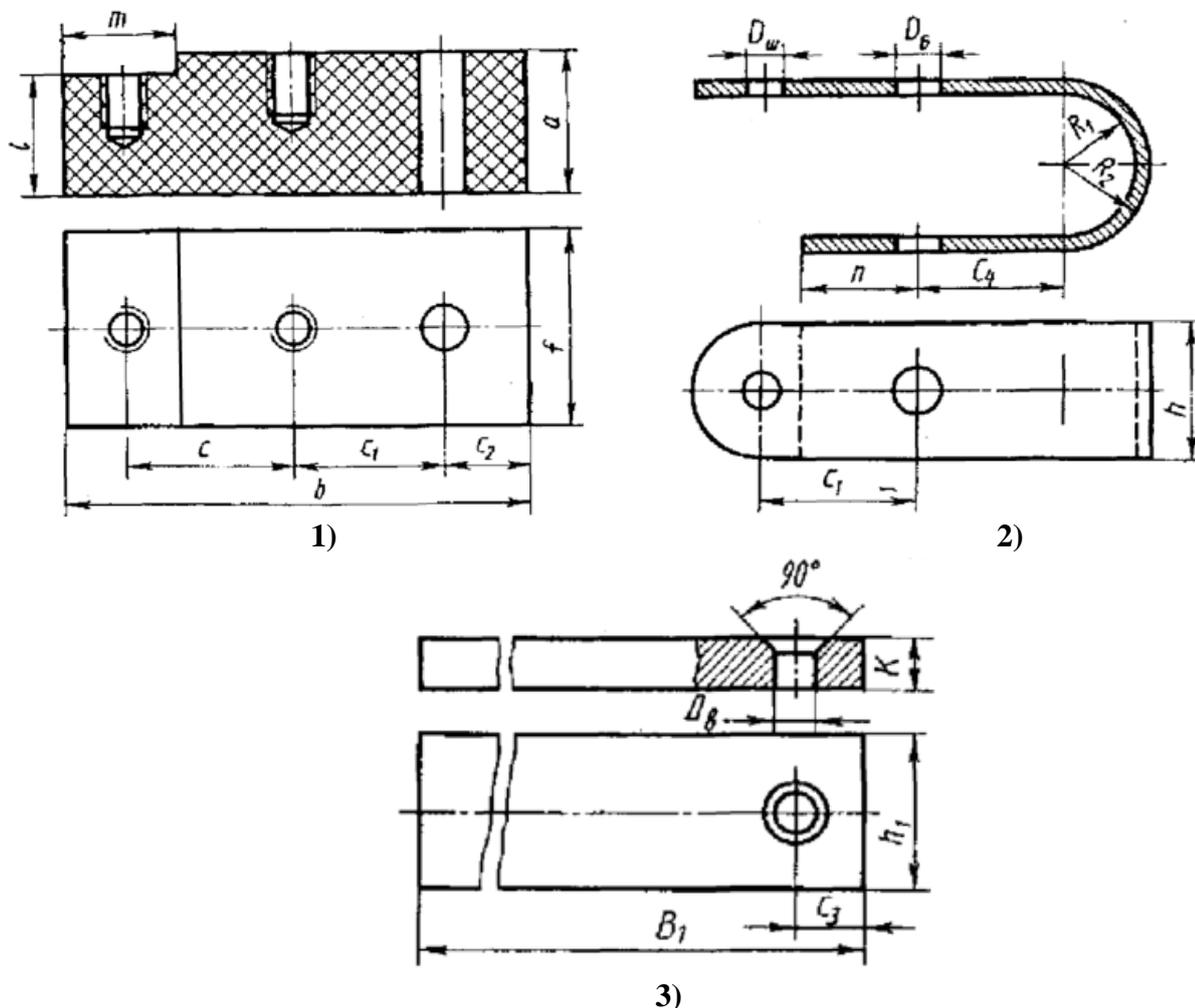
Детали и буквенные обозначения размеров деталей:
